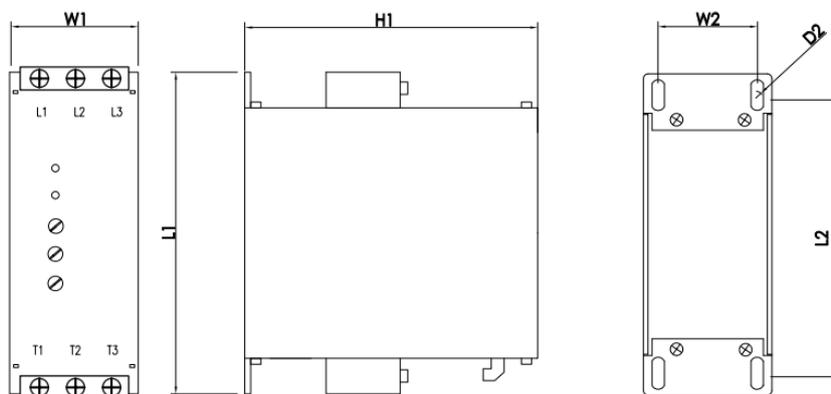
Габаритный чертеж при способе крепления винтами
